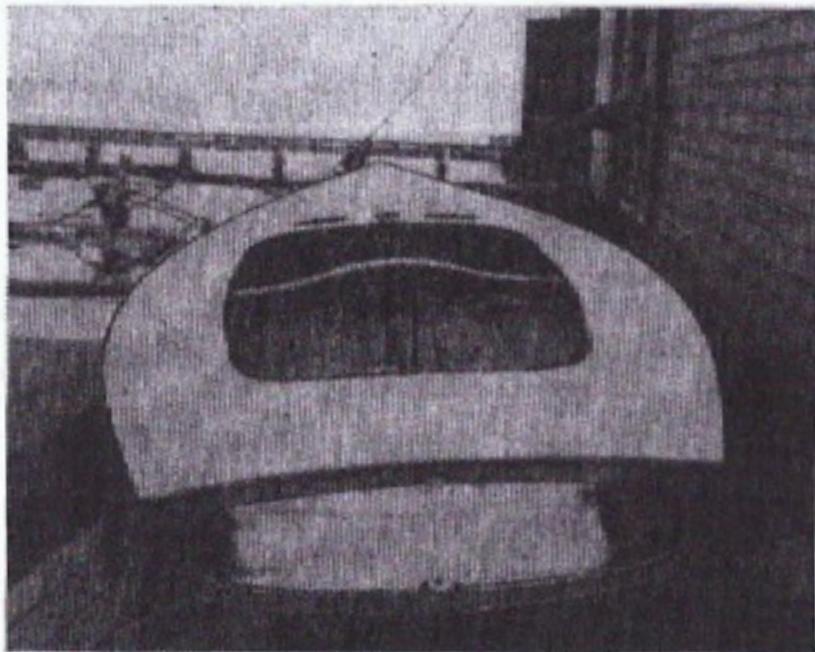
Общий вид швертбота скорлупной конструкции после постановки палубного настила.
